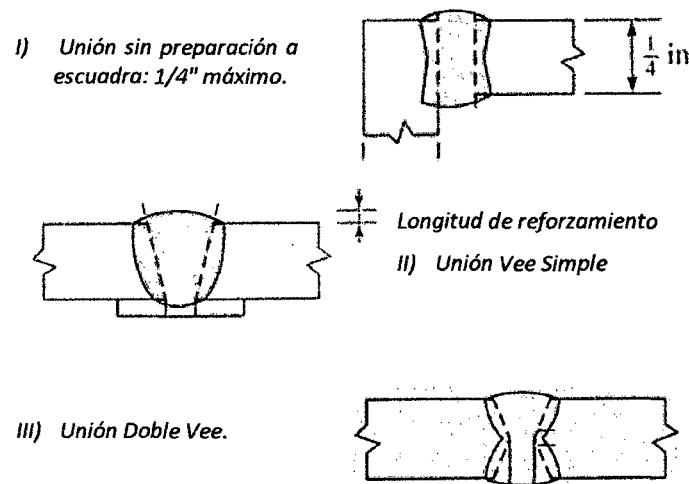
76: Tipos de Soldadura de Ranura (McCormac y Csernak, 2012).
